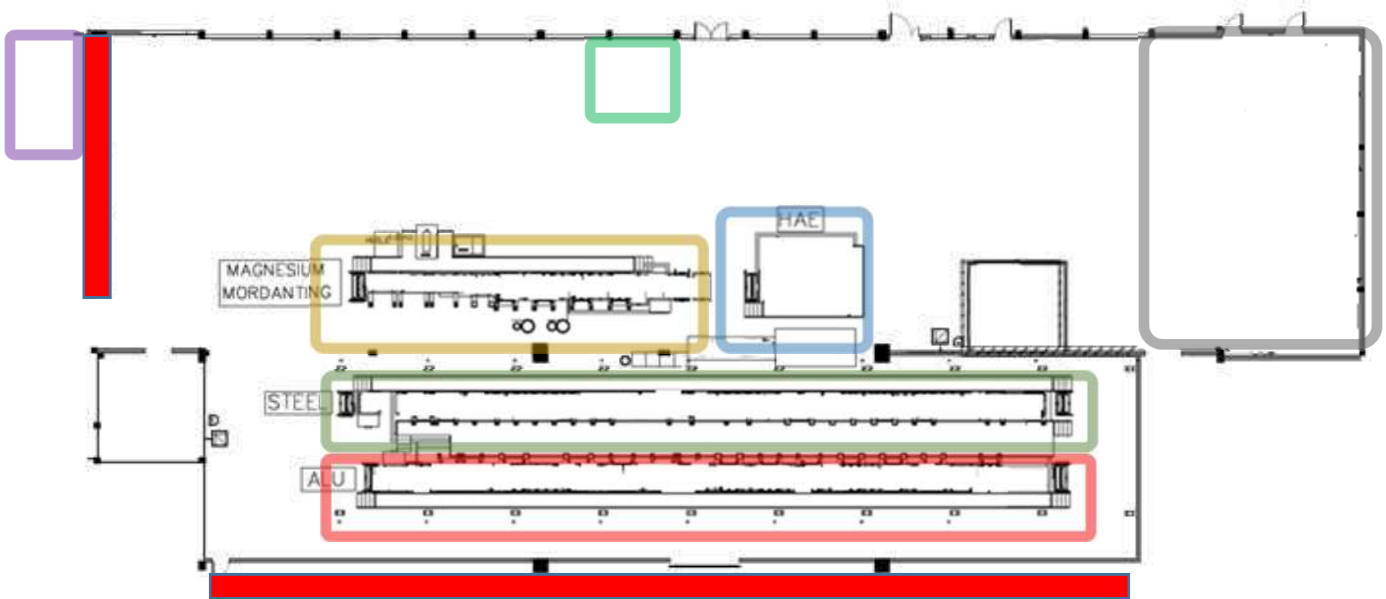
Plan des installations situées dans le local traitement de surface du bâtiment N1
